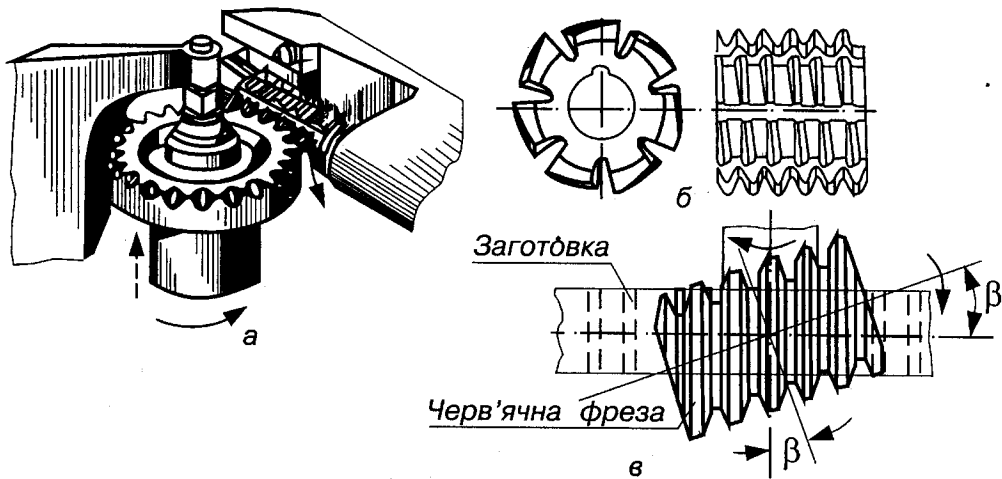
Нарізання зубчастих коліс за допомогою черв'ячної фрези
